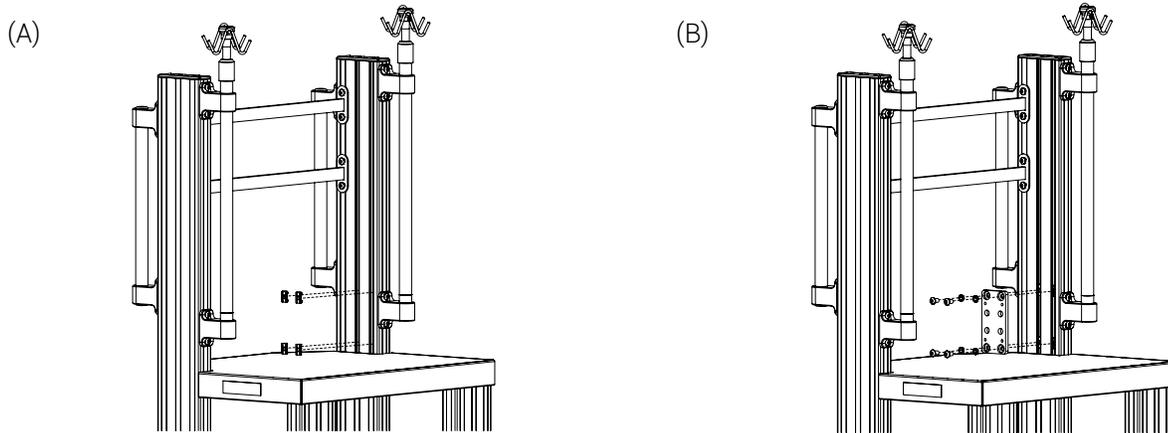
Pièces d'assemblage de la plaque-support et le système de montage Dräger avec adaptateur SLIDE
